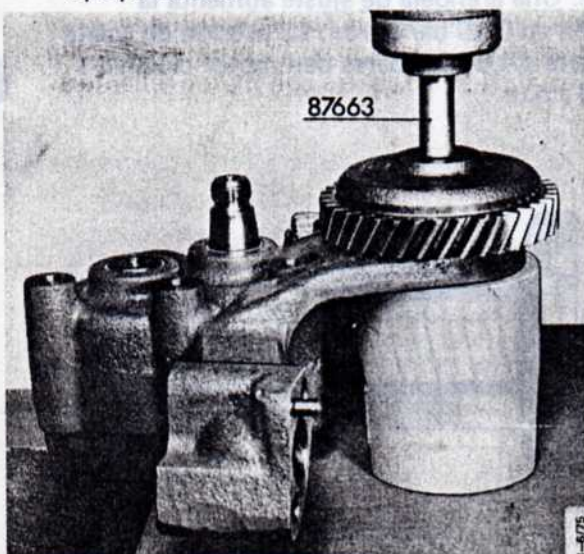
Se saca a presión el pivote del engranaje intermedio
